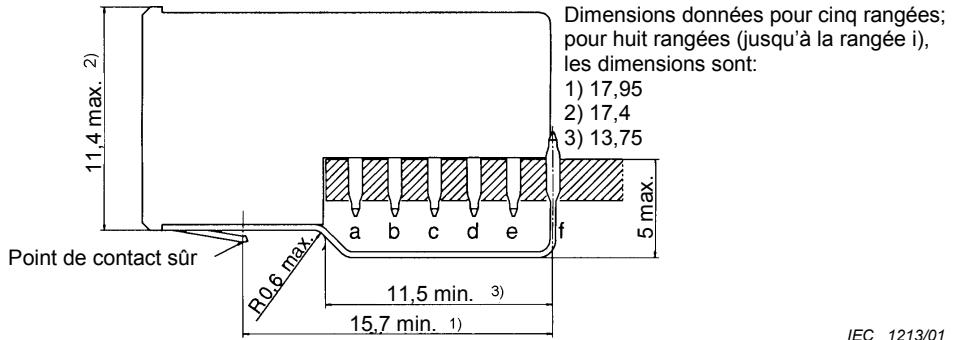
Dimensions d'accouplement de la coquille de blindage de la rangée z
